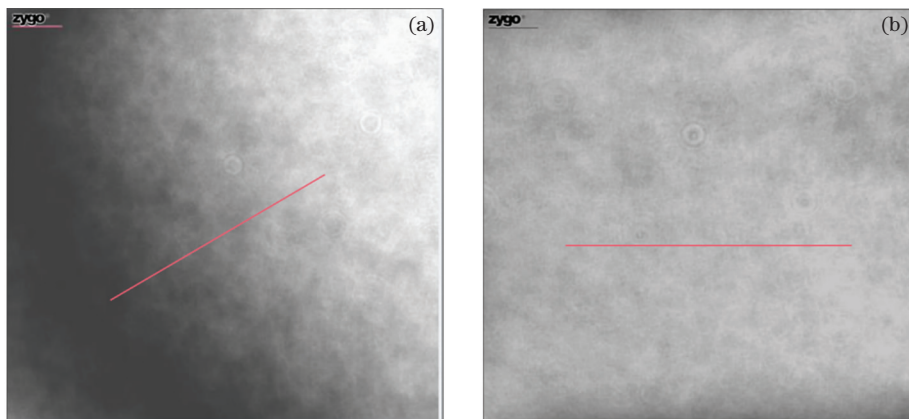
工件 2 和工件 3 干涉图的局部放大图。(a) 工件 2, 双转子运动; (b) 工件 3, 偏心双转子运动
